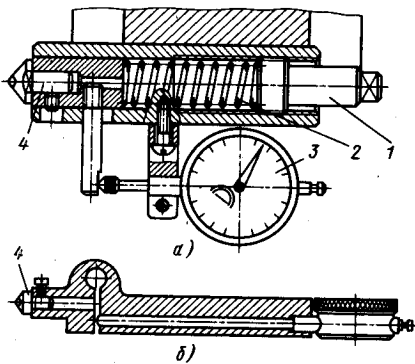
Державки для выглаживания поверхностей: а — с цилиндрической пружиной; б — с пружинящим корпусом; 1 — регулировочный винт; 2 — тарированная пружина; 3 — индикатор; 4 — наконечник с алмазом
